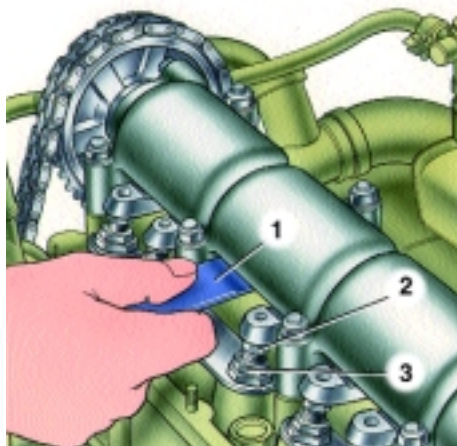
Проверка и регулировка зазора в механизме привода клапанов двигателя мод. 2106-70: 1 – плоский щуп; 2 – регулировочный болт; 3 – контргайка регулировочного болта
